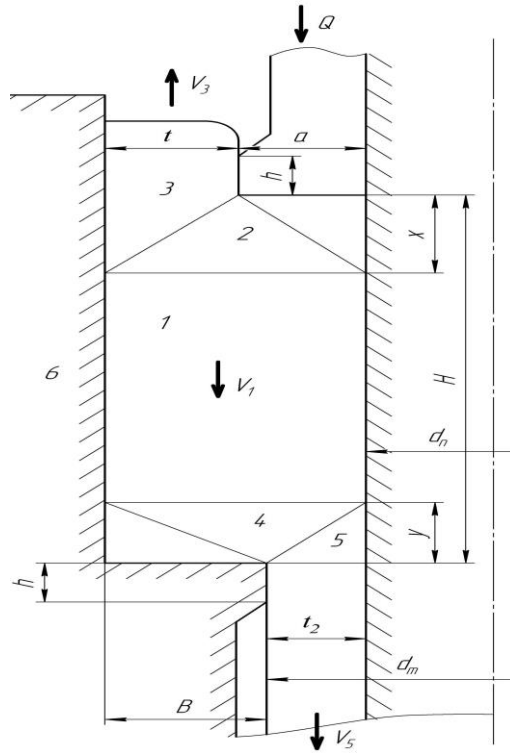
Розрахункова схема прямо-зворотного видавлювання
